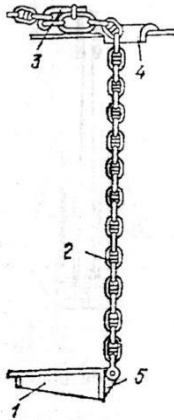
Крепление якорной цепи к корпусу судна с помощью жвака-галса:
